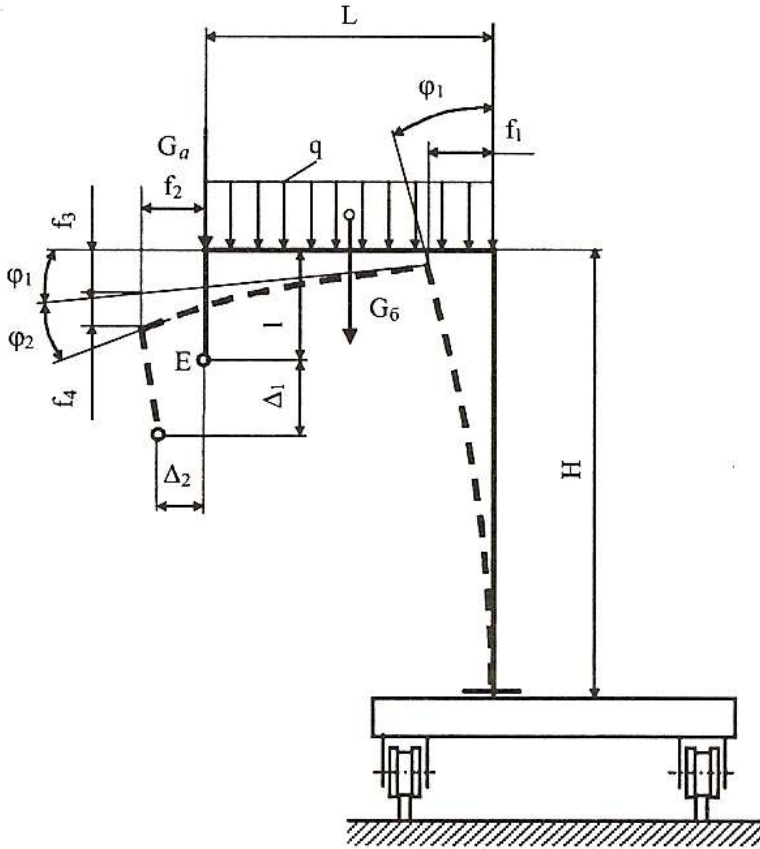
Розрахункова схема несучої конструкції глального зварювального візка [4]
